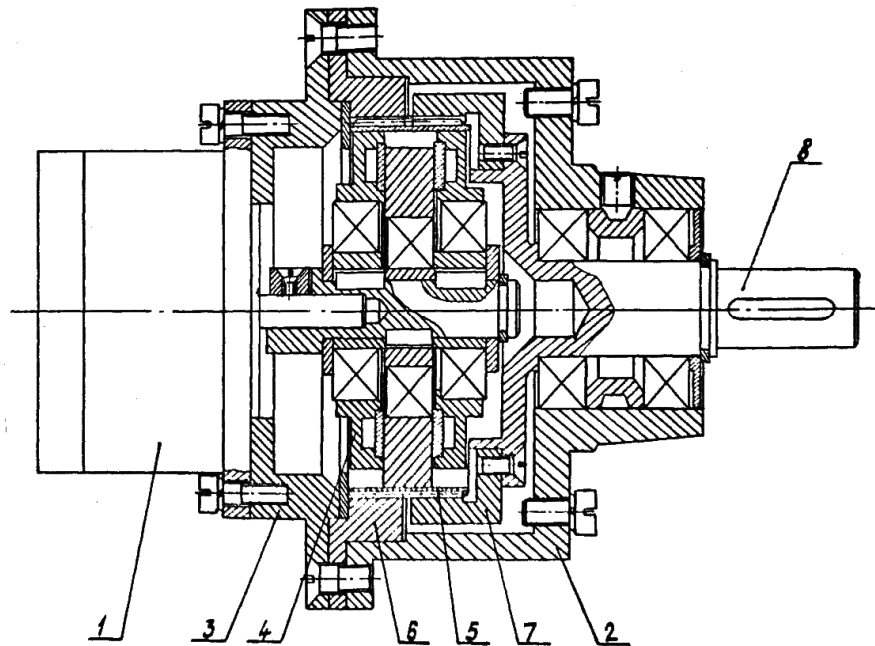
Общий вид модуля электромеханического малогабаритного: 1 — электродвигатель; 2 — корпус; 3 — крышка корпуса; 4 — генератор; 5 — колесо гибкое; 6 — колесо жесткое; 7 — полу муфта зубчатая; 8 — вал выходной.
